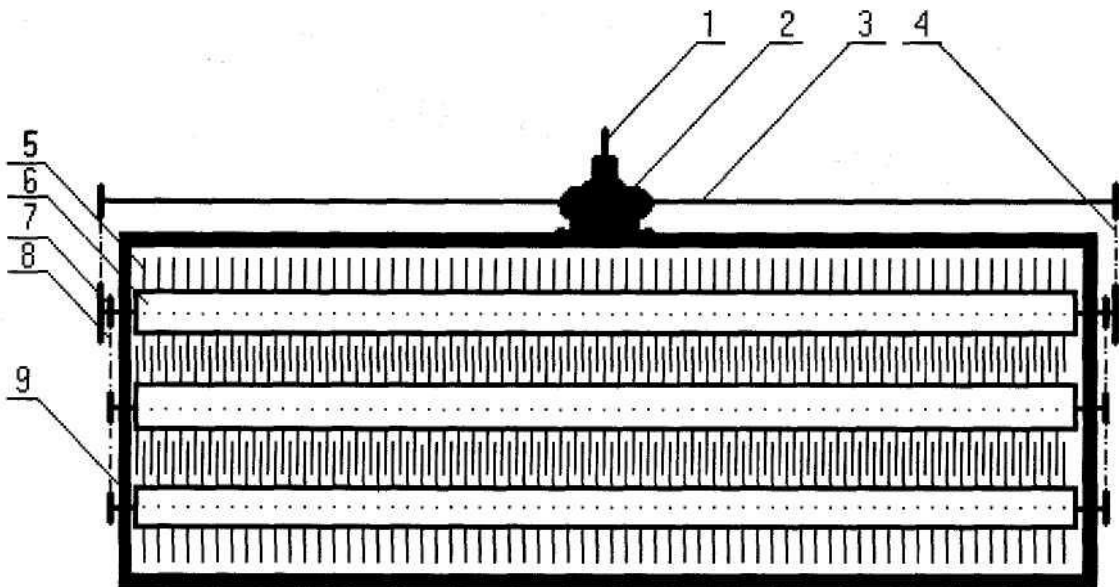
Схема агрегату для обробітку ґрунту: 1- приводний вал; 2 - редуктор конічний; 3- вихідний вал редуктора; 4, 8 - ланцюгові передачі; 5 – зуби; 6 – барабан; 7-вал приводу першого барабану; 9- рама
